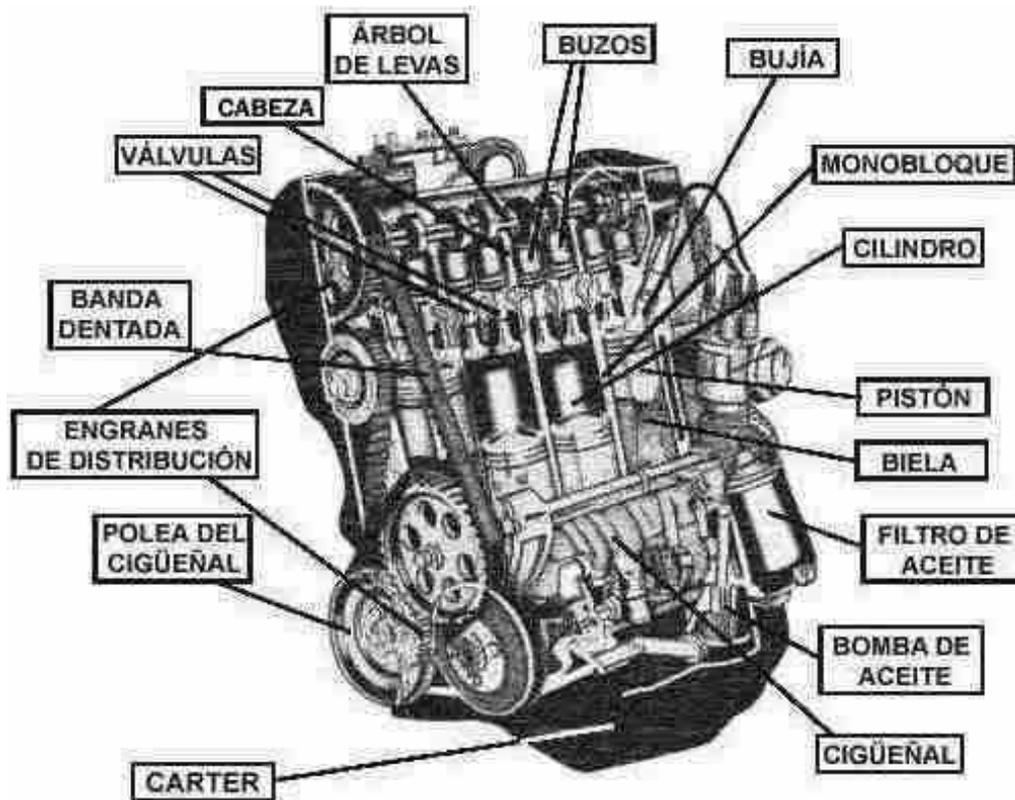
El motor de combustión interna con algunas de sus partes más importantes.³
